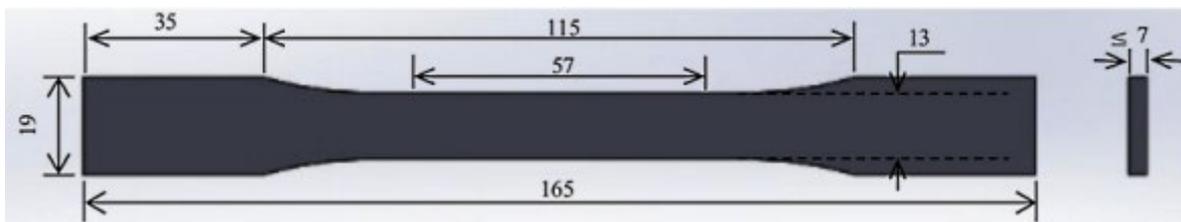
Dimensões dos corpos de prova para ensaio de tração em polímeros (medidas em mm)
